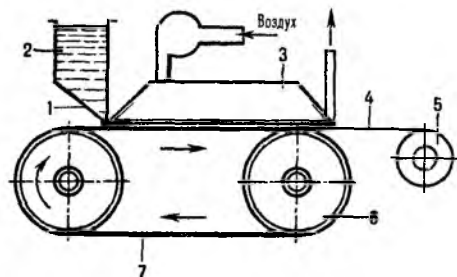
Формование пленок поливом: 1—фильера; 2—емкость с р-ром полимера; 3—сушильная камера; 4—пленка полимера; 5—смотывающее устройство; 6—барабан транспортера; 7—транспортерная лента.
